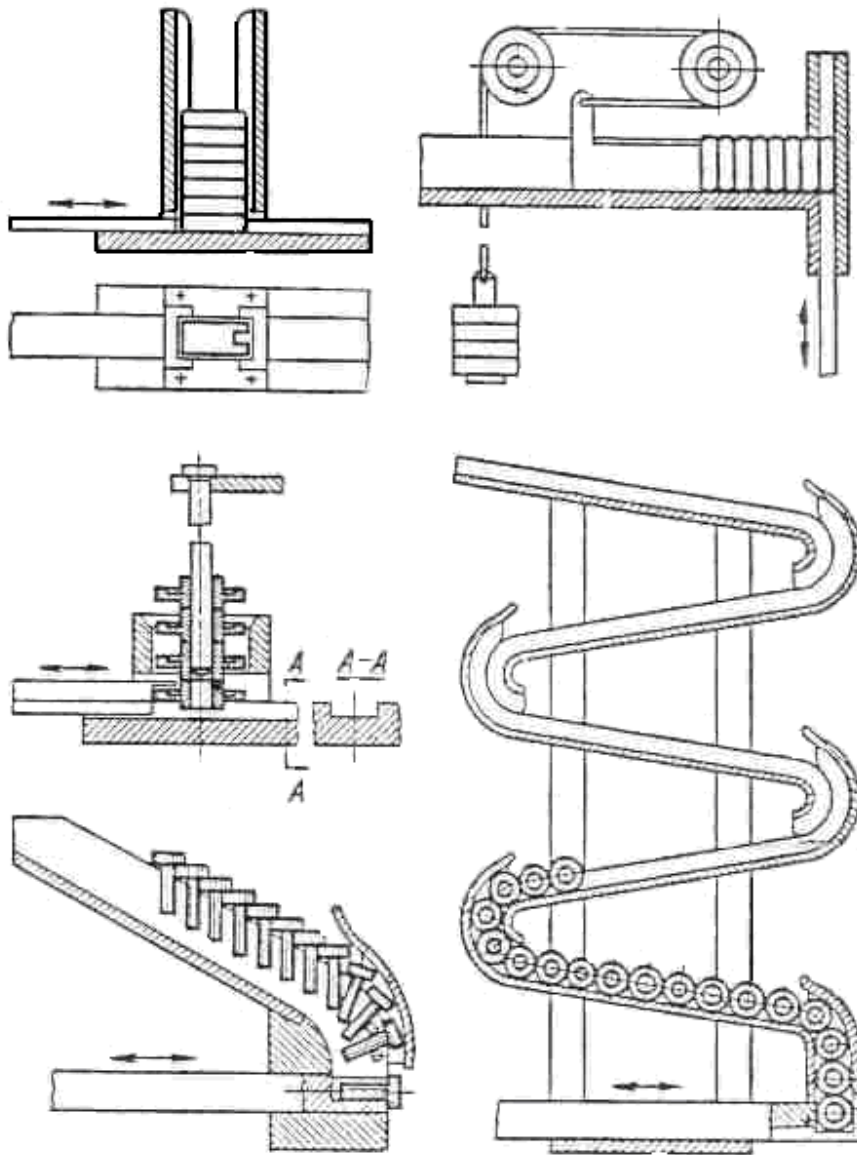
Магазиные загрузочные устройства для заготовок, закладываемых штабелем в один ряд
